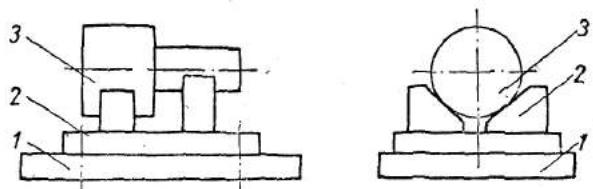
Приклад розміщення заготовки на тактовому столі:
